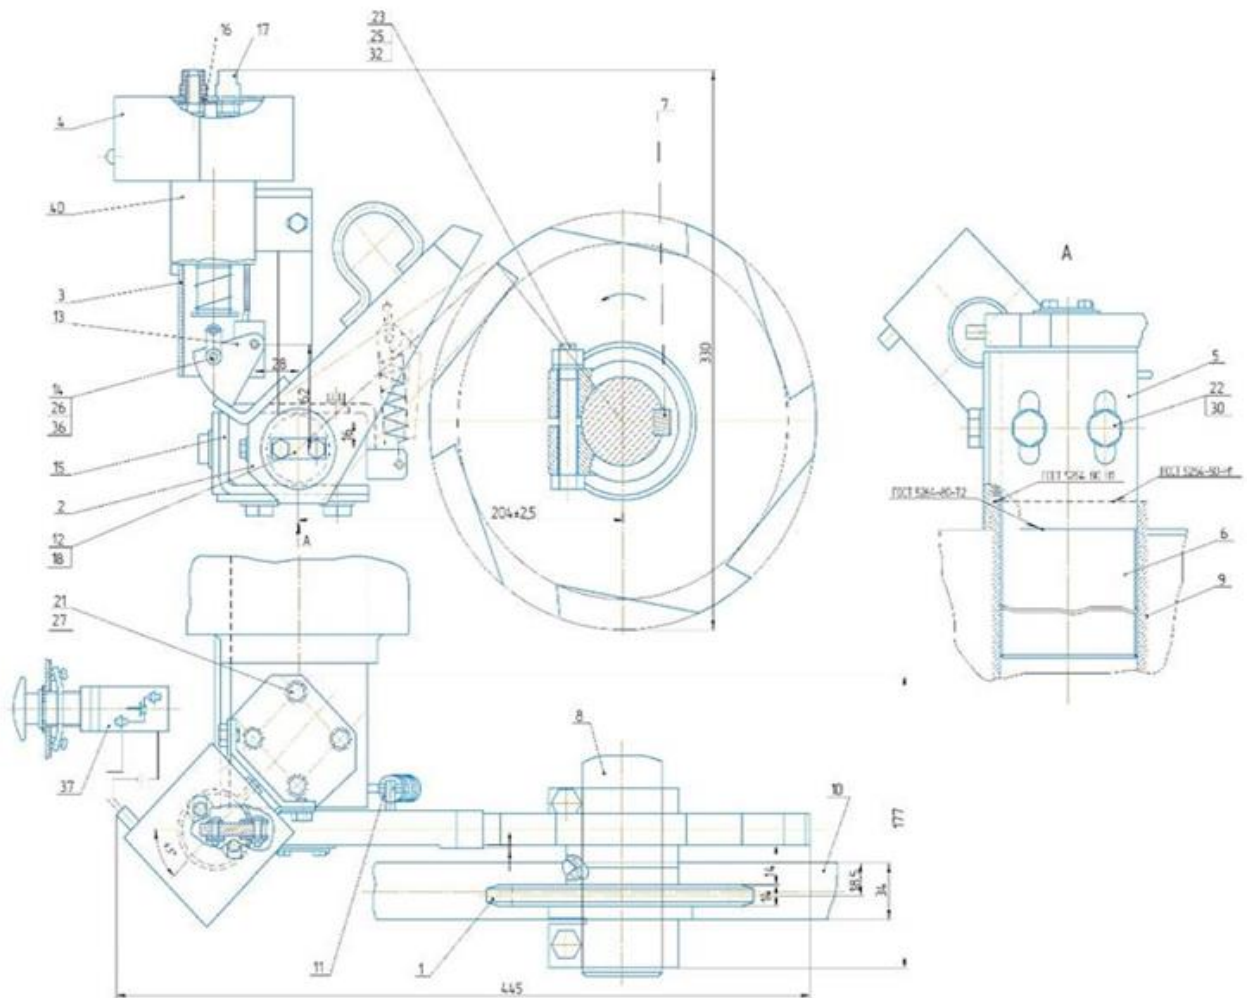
Конструкція розробленого механізму для аварійного зупинення жатки комбайна
